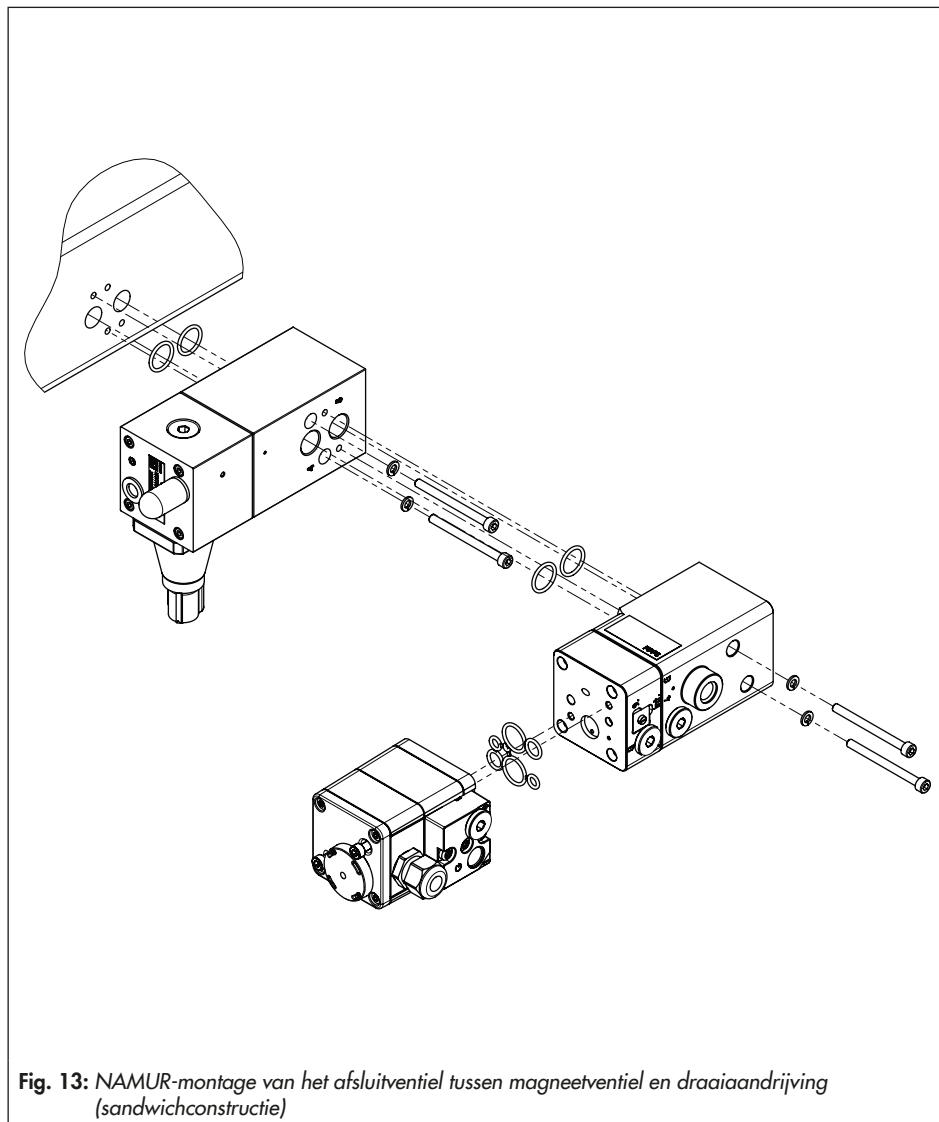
NAMUR-montage van het afsluitventiel tussen magneetventiel en draaiaandrijving (sandwichconstructie)
